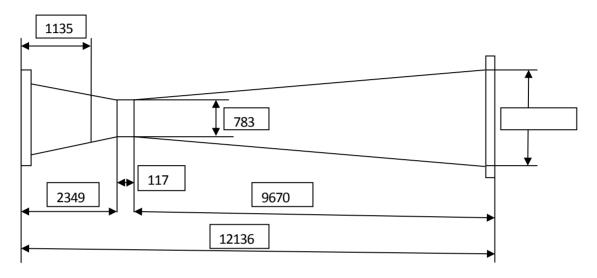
Venturi para colocar en el ducto de Planta Vieja a la entrada del ciclón lavador
